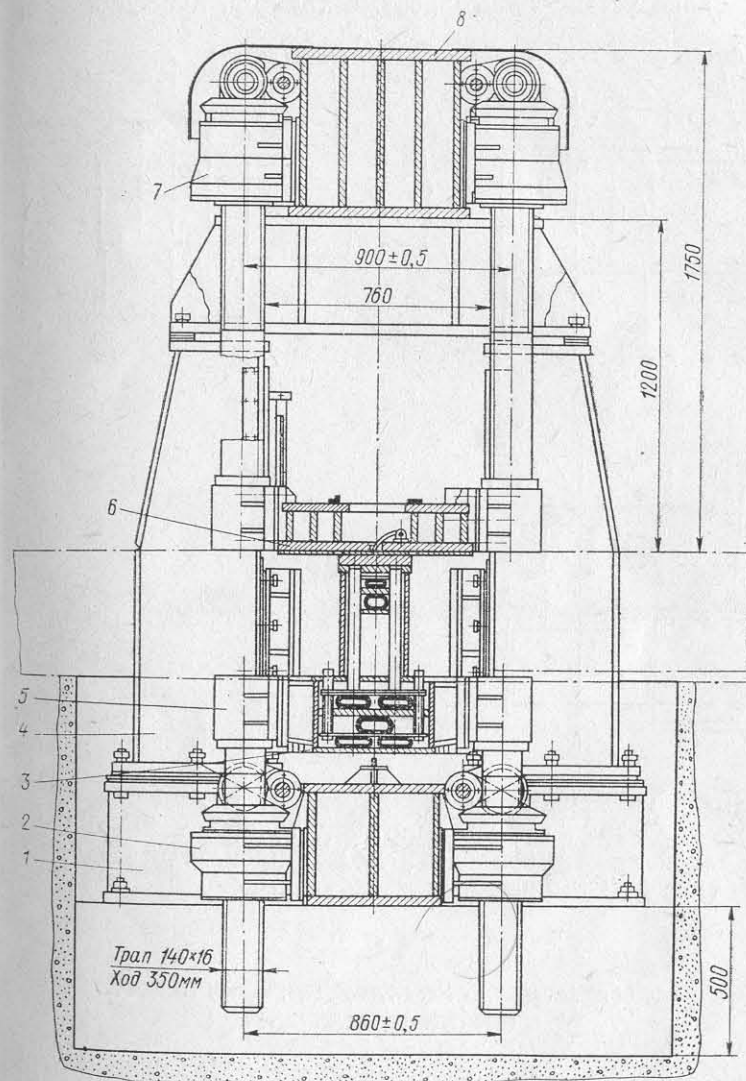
Схема устройства стенда для автоматической сварки полотнищ и секций толщиной до 15 мм.
